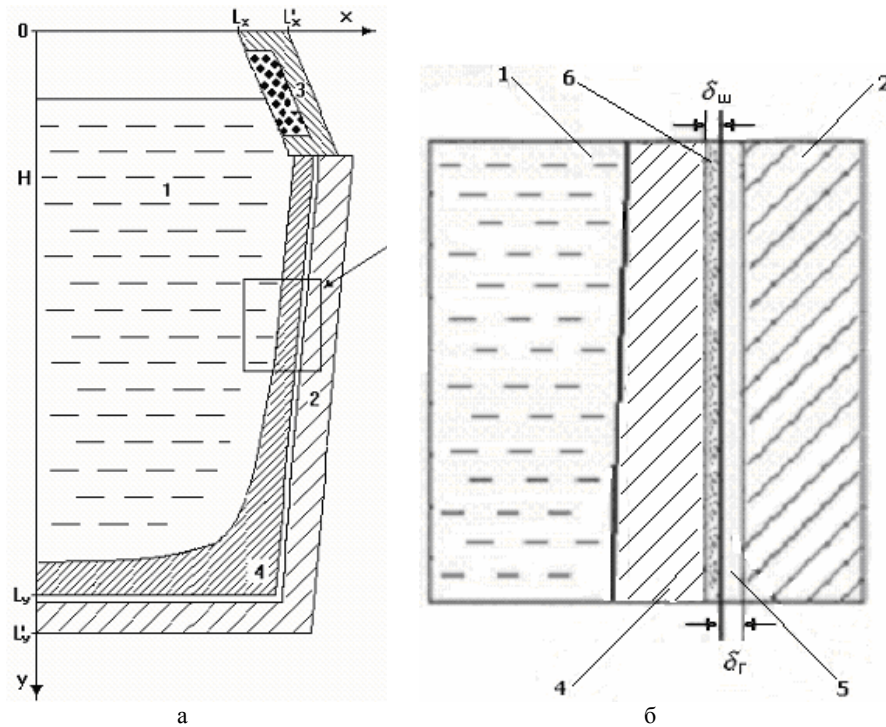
Схема исследуемой области: 1 – расплав стали; 2 – стенка изложницы; 3 – прибыльная надставка; 4 – затвердевший металл; 5 - газовый зазор; 6 – шлаковый гарнисаж. а) изложница; б) увеличенный фрагмент на границе слиток – изложница.
